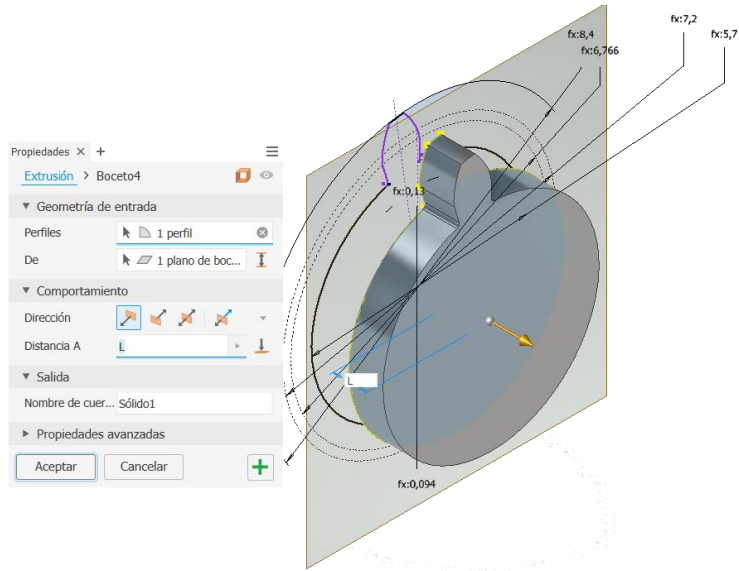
Proyección del perfil del diente en el plano de trabajo.
